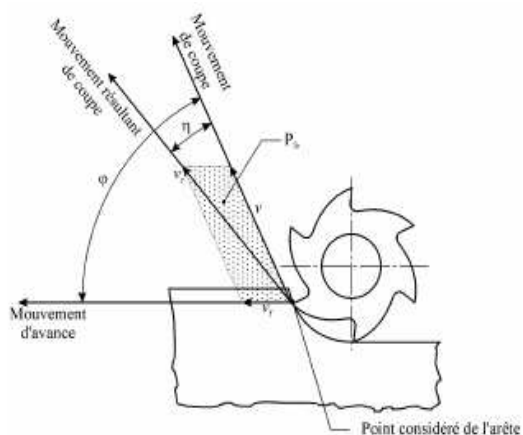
Mouvements de l'outil et de la pièce en fraiseuse
